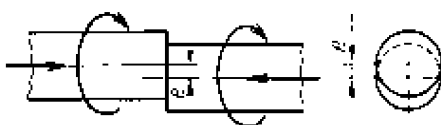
Схема процесса орбитальной сварки
